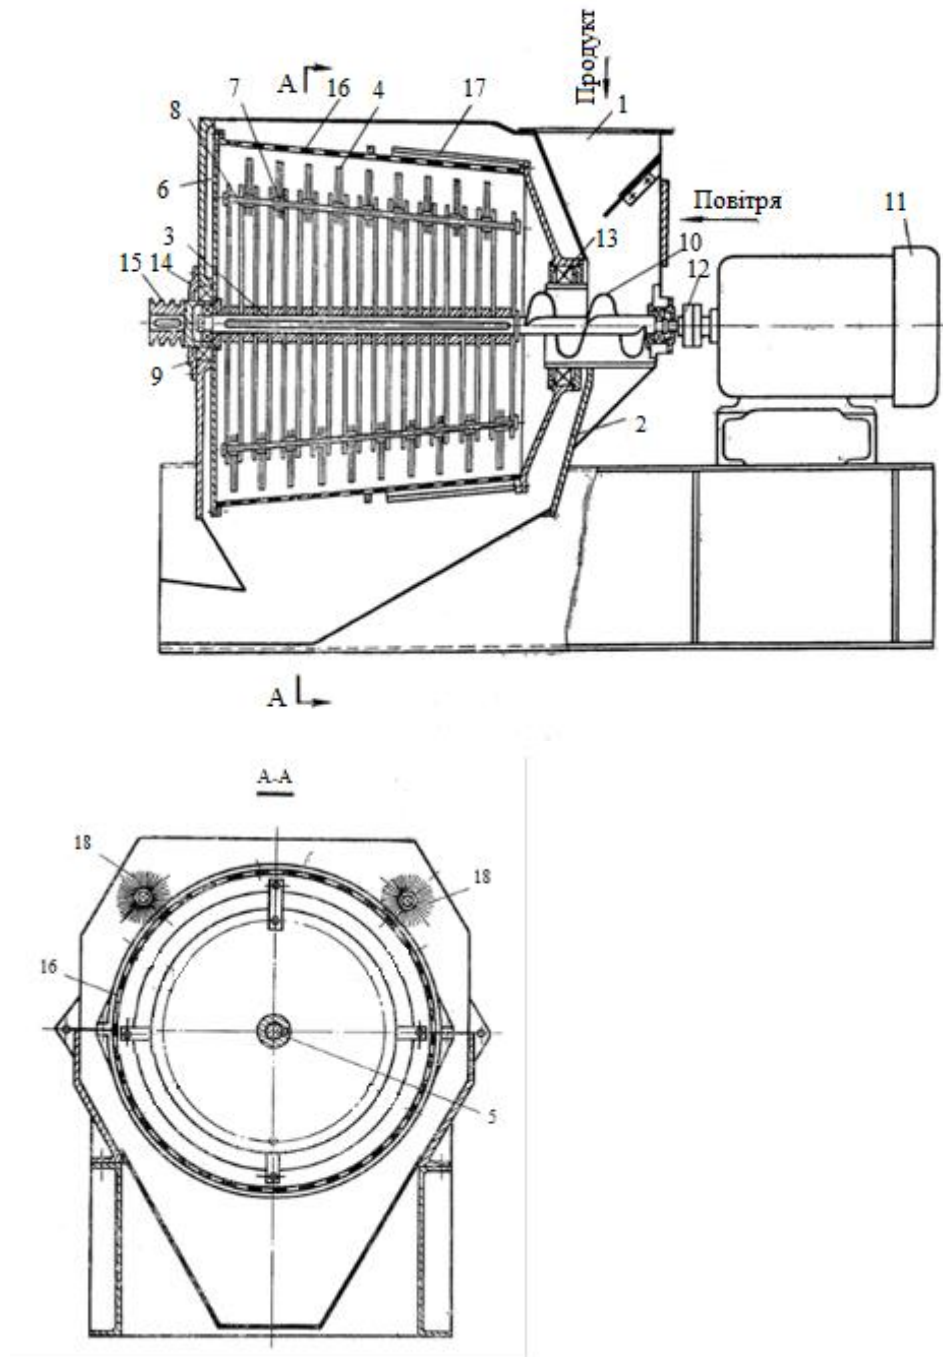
Молоткова дробарка: 1 – завантажувальний пристрій; 2 – корпуса; 3 – ротора; 4 – молотки; 5 – валу; 6 – барабан; 7 – втулки; 8 – вісь; 9, 13, 14 – підшипники; 10 – шнек; 11 – електродвигун; 12 – муфта; 15 – шків; 16 – перфорована поверхня; 17 – деки.
